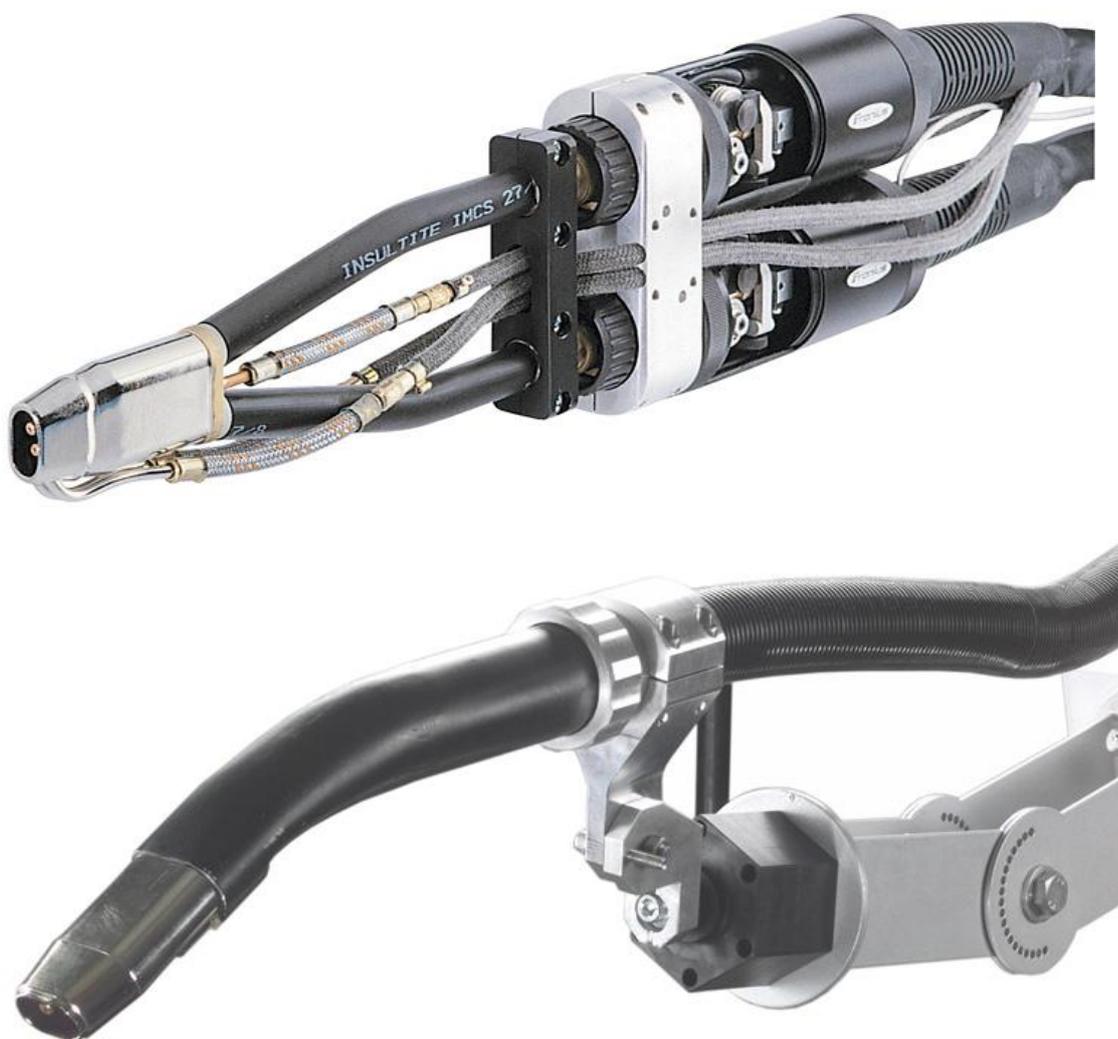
Сварочные горелки Robacta Drive Twin и Robacta Twin Compact.
